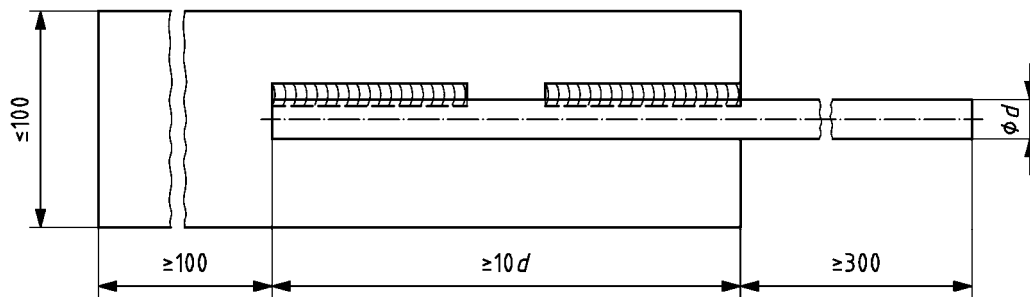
Probe für Zugversuch für andere Verbindungen (einseitige Flankenkehlnähte)
